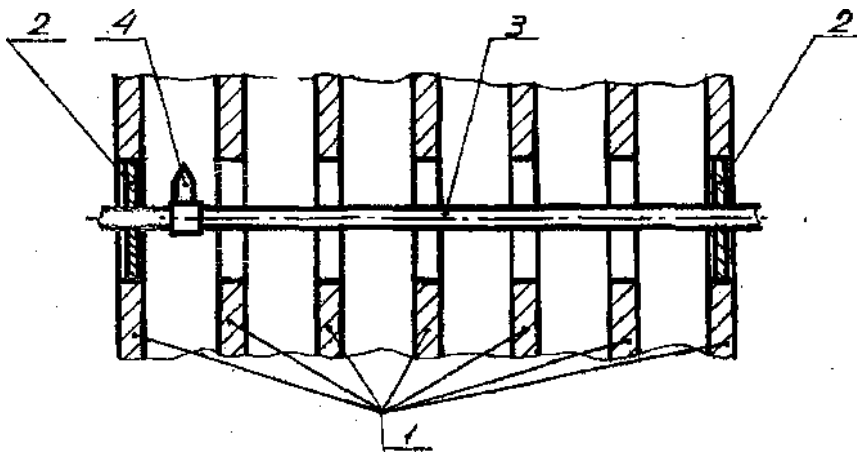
Міжопорна схема базування розточувального пристрої в постелях корінних підшипників КШМ
